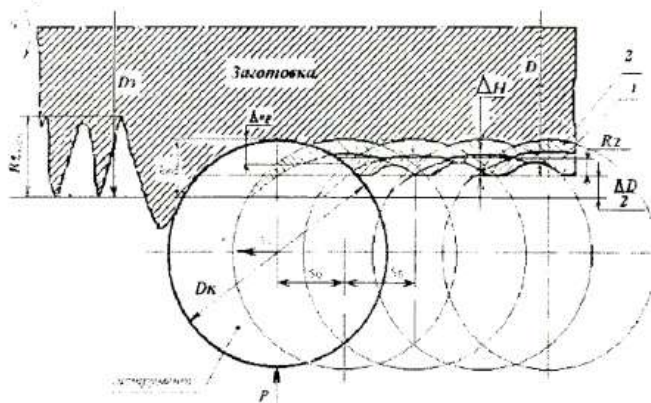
Схема деформації поверхневого шару металу під час обкатування кулькою циліндричної заготовки:
